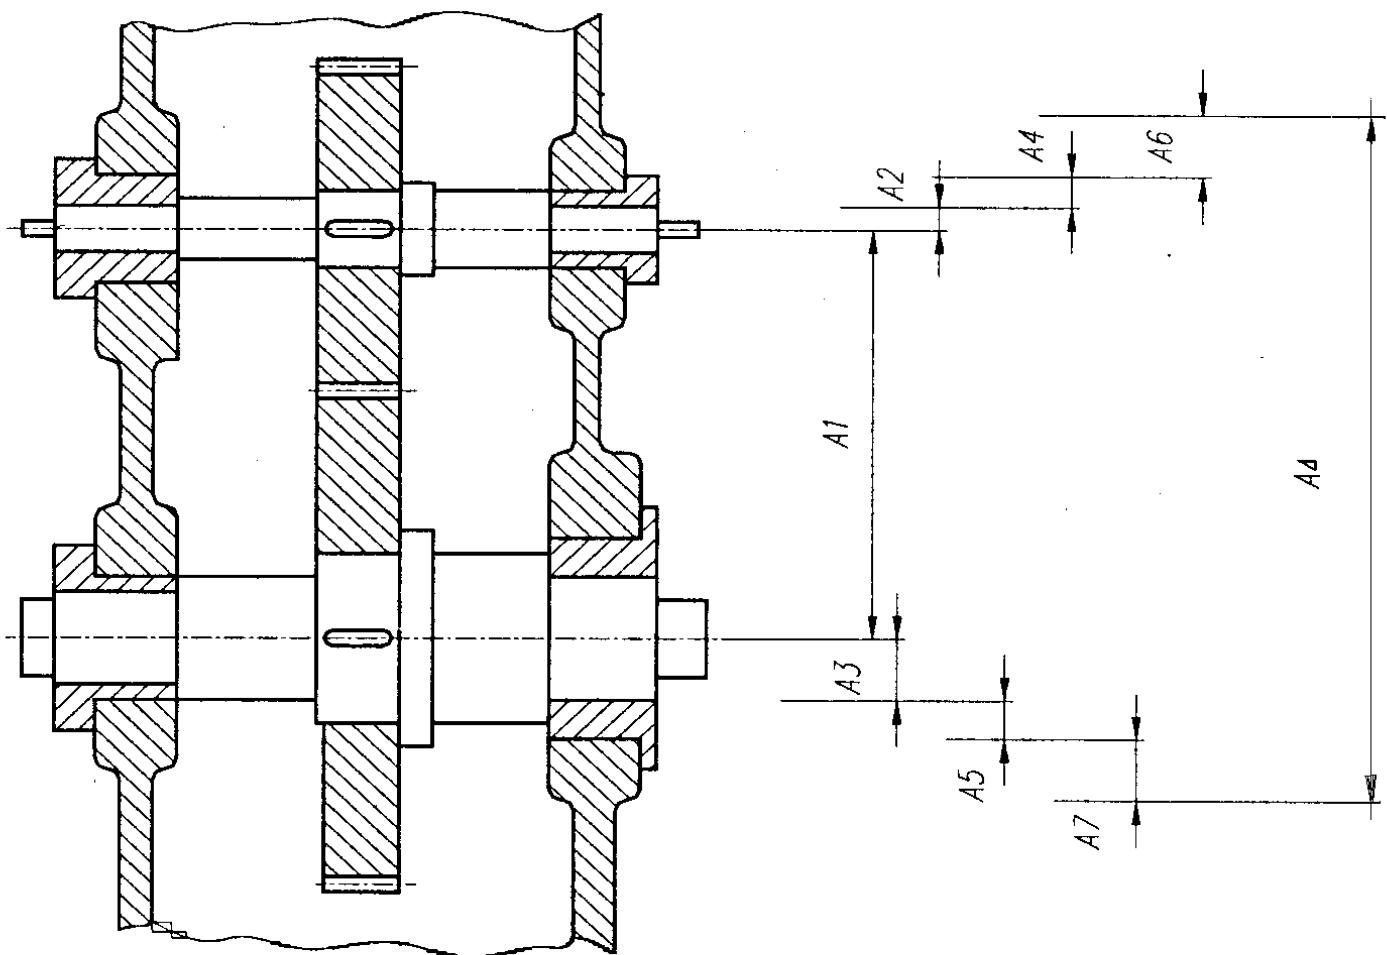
Размерная цепь для межосевого расстояния цилиндрической зубчатой передачи
